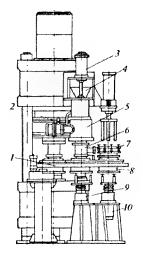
Формовочный агрегат с поворотным столом и задувной машиной: 1 поворотный клапан; 3— шибер; 4— бункер; 5— вадувная машина; 6— приставка; 7— пивмосъемник; 8— пресс-форма; 9— гадроцилитар прижима;
